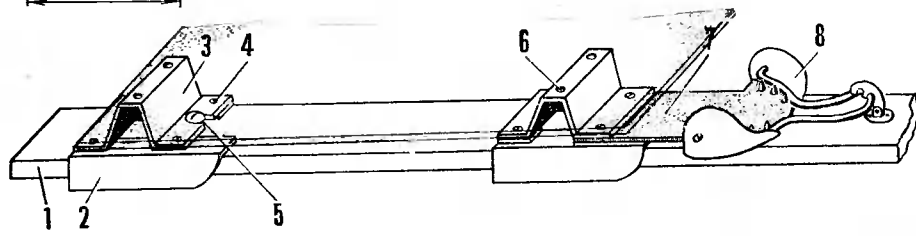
Узлы крепления корпуса прогулочного компромисса:
